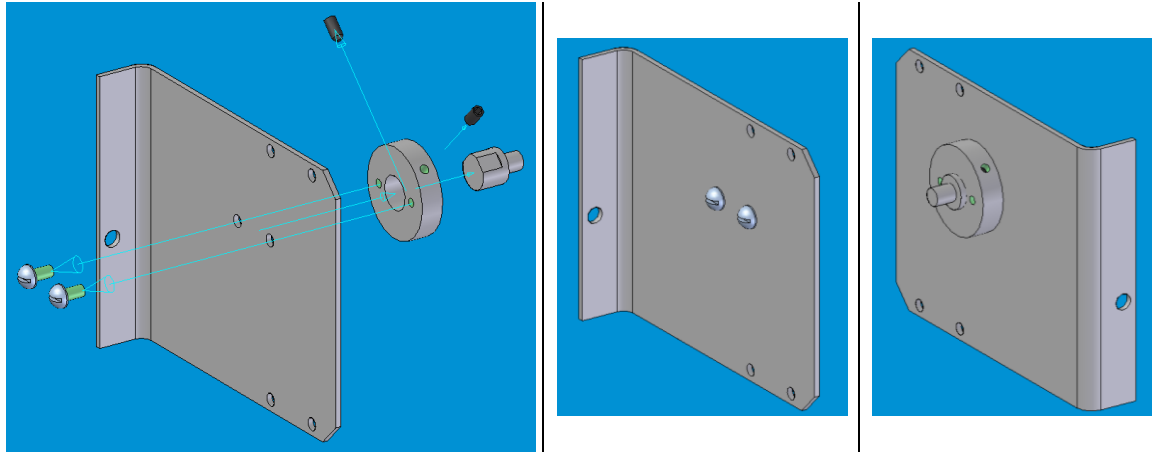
Conjunto de piezas unidas a la tapa del lado izquierdo de la caja del telémetro.
